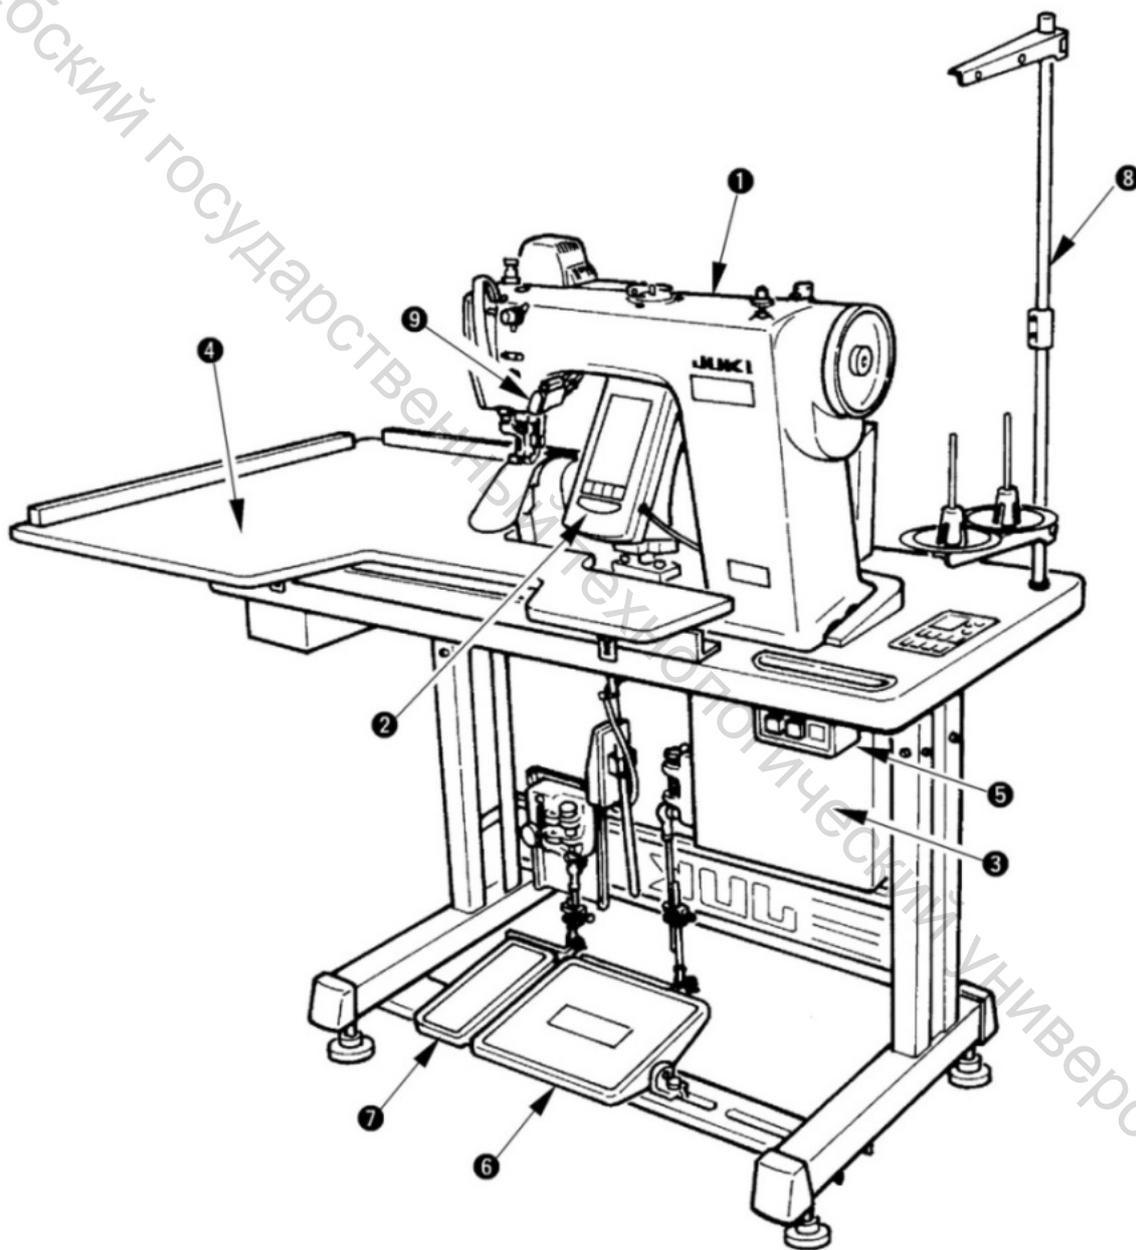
Общий вид машины DP-2100 Juki:
